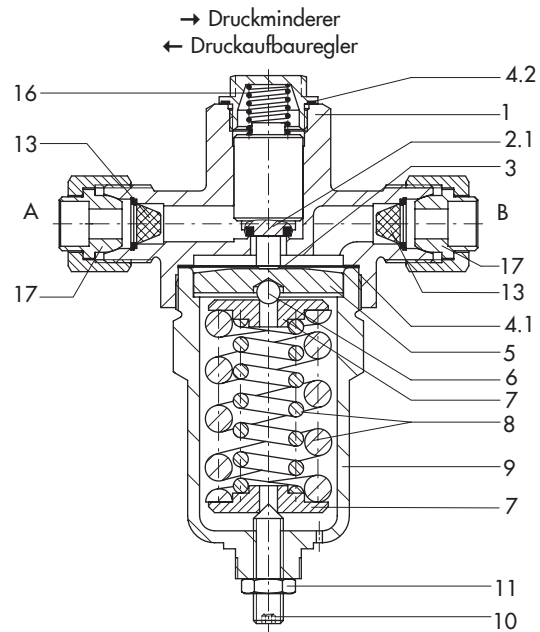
Druckaufbauregler oder Druckminderer Typ 2357-1 (PN 50)
